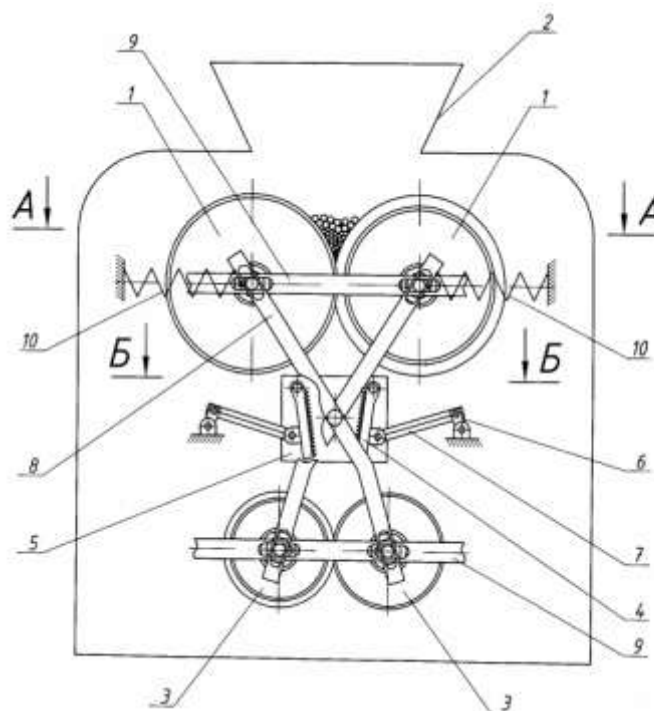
Схема пресс – валкового агрегата для измельчения мелкокусковых материалов
